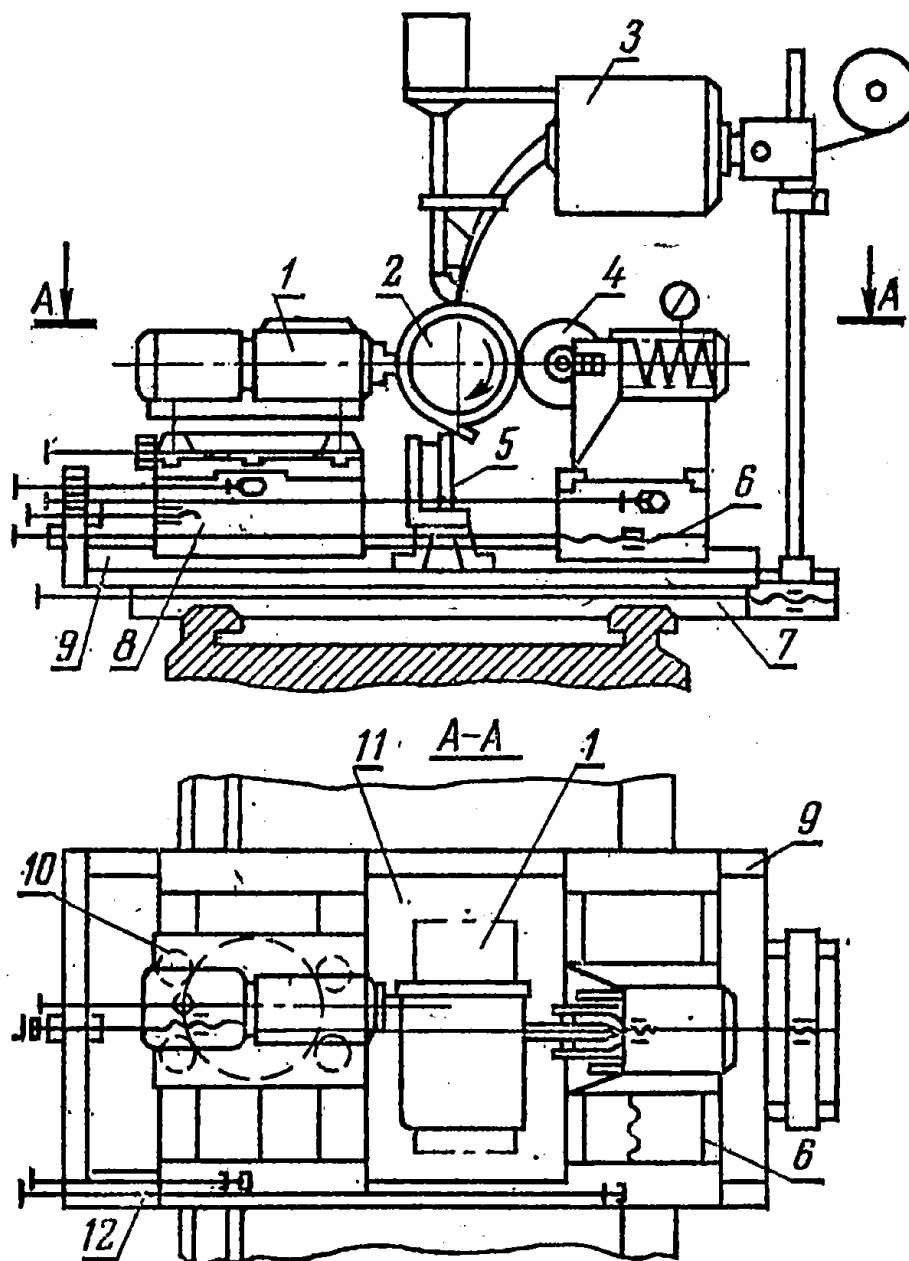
Схема установки для наплавки цилиндрических деталей под флюсом с одновременным фрезерованием и накаткой роликом:
